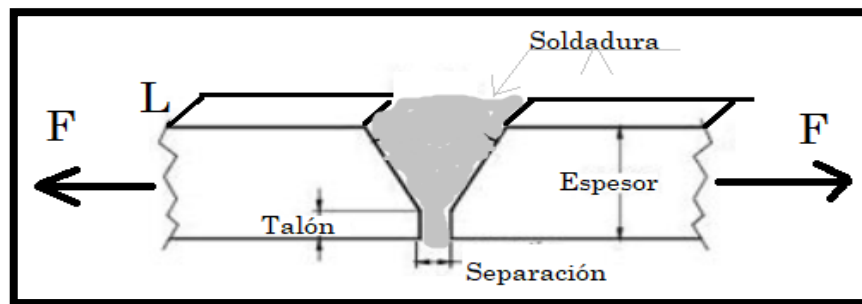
D. C. L. Para soldadura sometida a fuerzas de tracción
